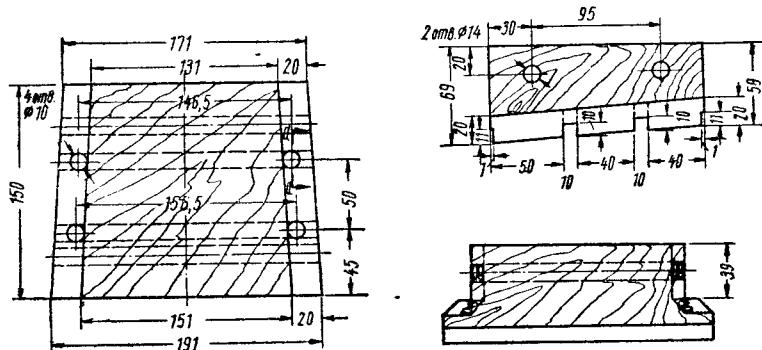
а. Рабочий чертеж боковой стеики мундштука
